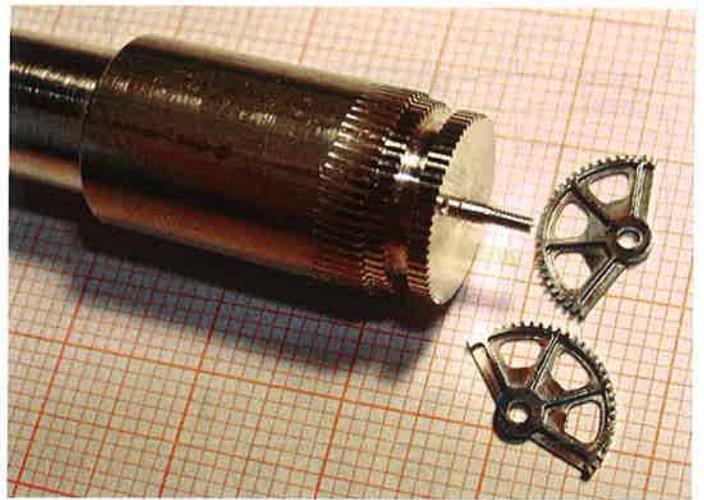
Die Zahnsegment-Teile wurden auf einen Fräsdorn mit einem M2-Gewindezapfen befestigt und „im Paket“ wie bei Abb. 13 die winzige Zahnung eingefräst
